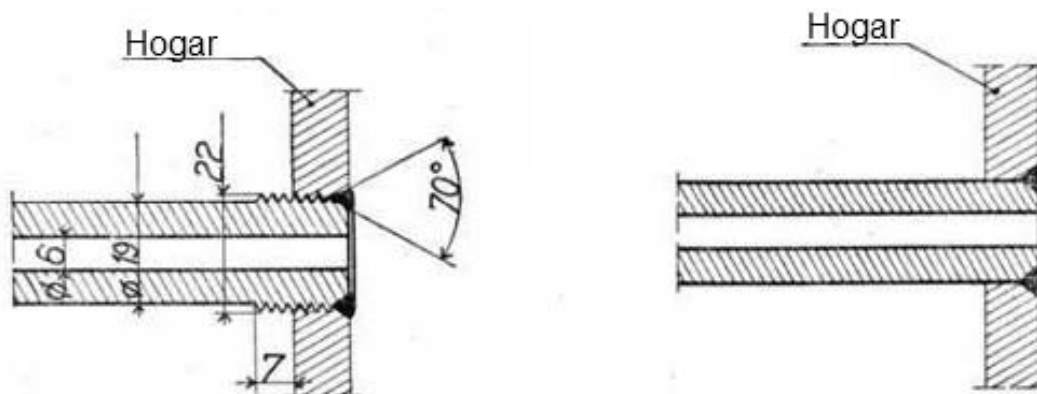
Virotillo en acero con cabeza soldada. Fig.143 – Virotillo en acero sin rosca, con cabeza soldada
